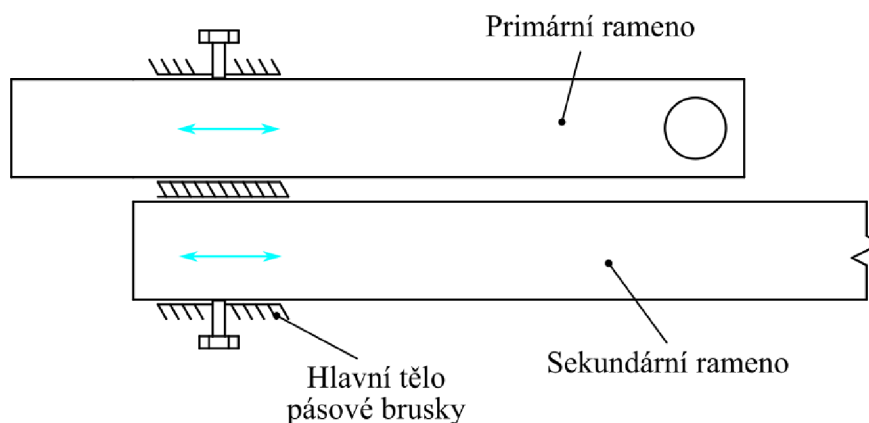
Uspořádání výsuvných ramen – varianta 1
